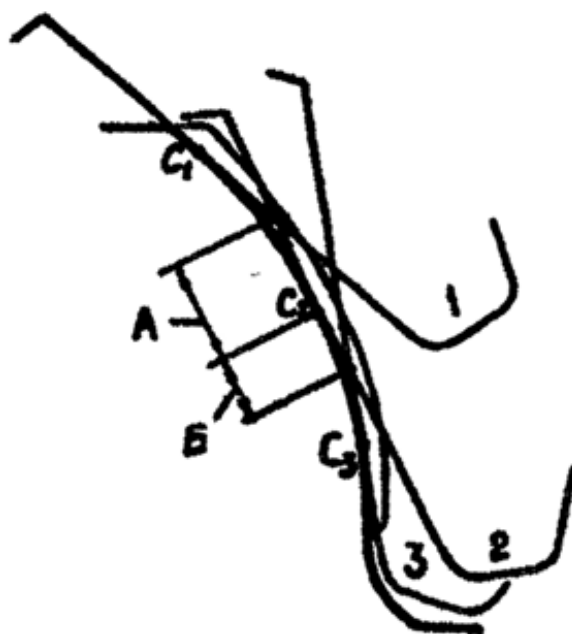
Схема резания зубьев червячной фрезы при чистовом зубофрезеровании.
